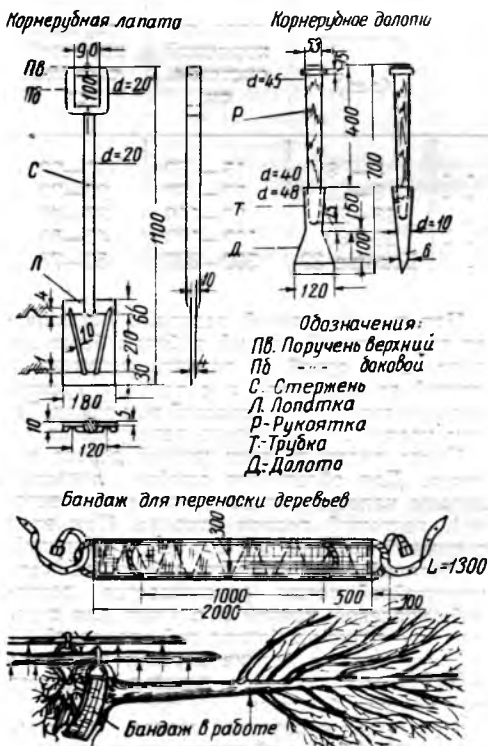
Инструменты и приспособления для пересадки деревьев.
